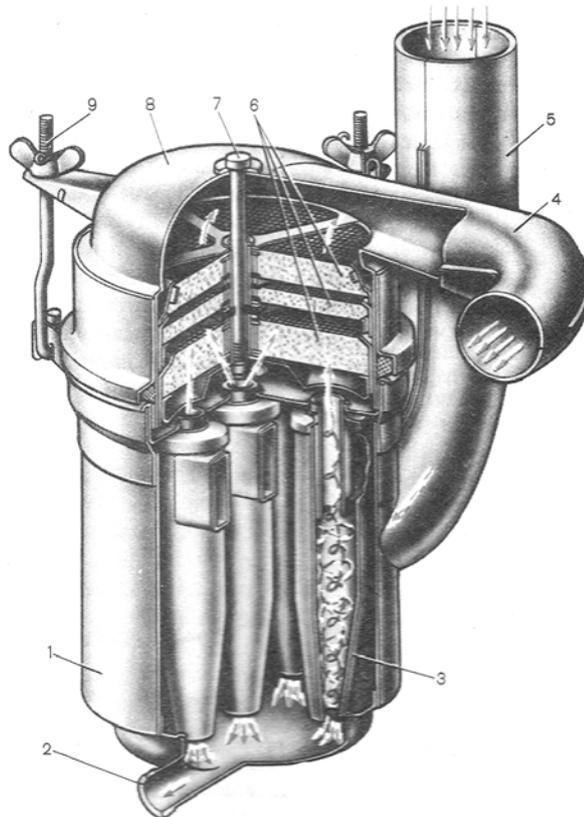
Комбинированный сухой воздушный фильтр двигателей типа СМД: 1 – корпус; 2 – патрубок для отсоса пыли; 3 – циклон; 4 – патрубок для отвода воздуха; 5 – патрубок для подвода воздуха; 6 – кассеты фильтрующего элемента; 7 и 9 – стяжные болты; 8 – крышка фильтра;
